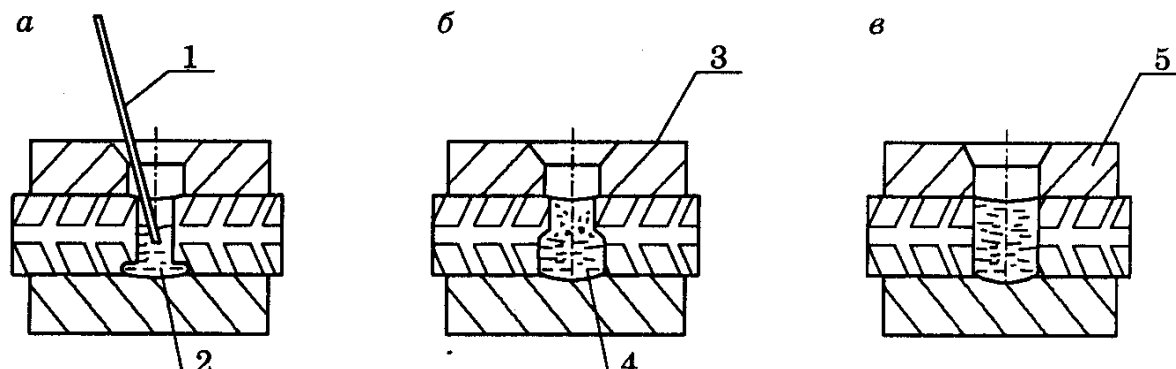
Техника ванной сварки в графитовых формах:
